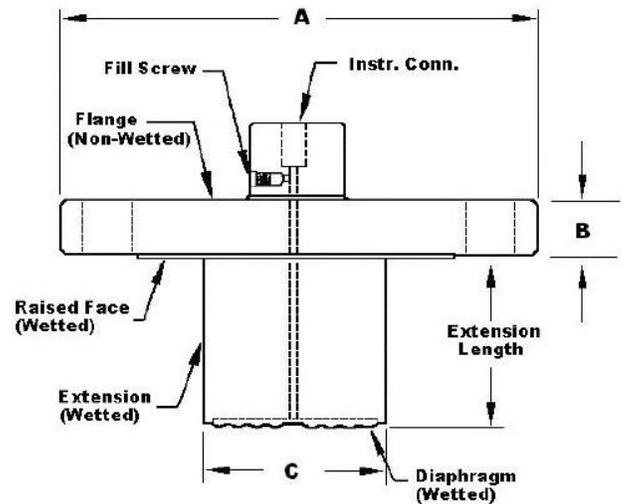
Druckmittler-Abmessungen (bündiger Flansch)
